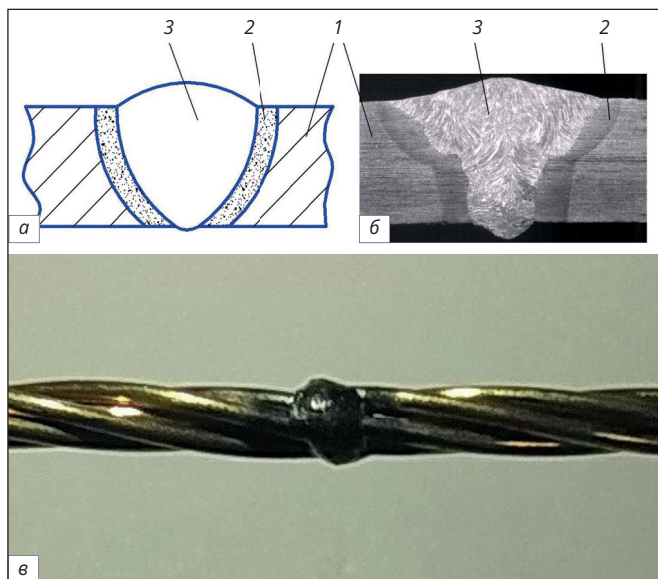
Схема строения (а) и макрошлиф (б) сварного соединения, где 1 – основной металл; 2 – переходная зона; 3 – сварной шов; фото образца металлокорда конструкции 1 + 5х0,40НТ со сварным швом (в)
